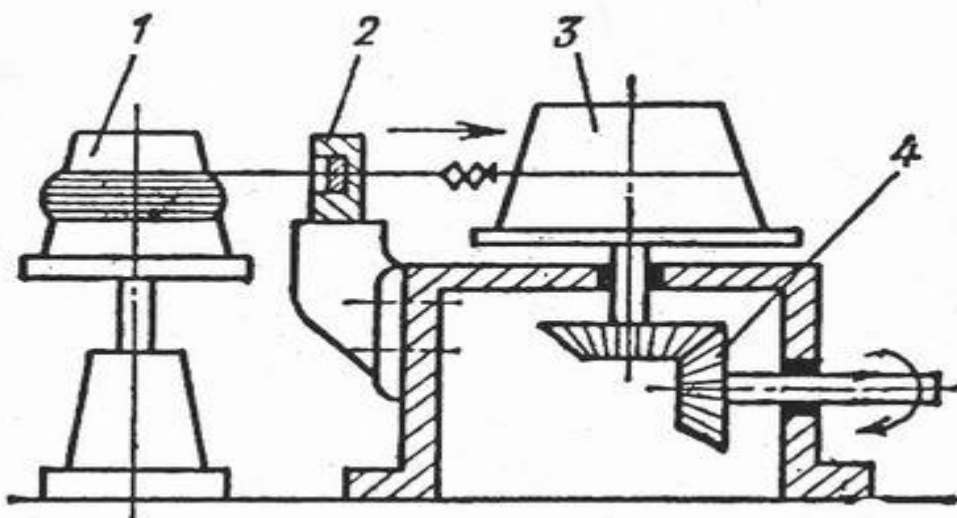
Принципиальная схема барабанного волочильного стана с вертикальной осью. 1 – вертушка; 2 – волока; 3 – барабан; 4 – редуктор и зубчатая передача
